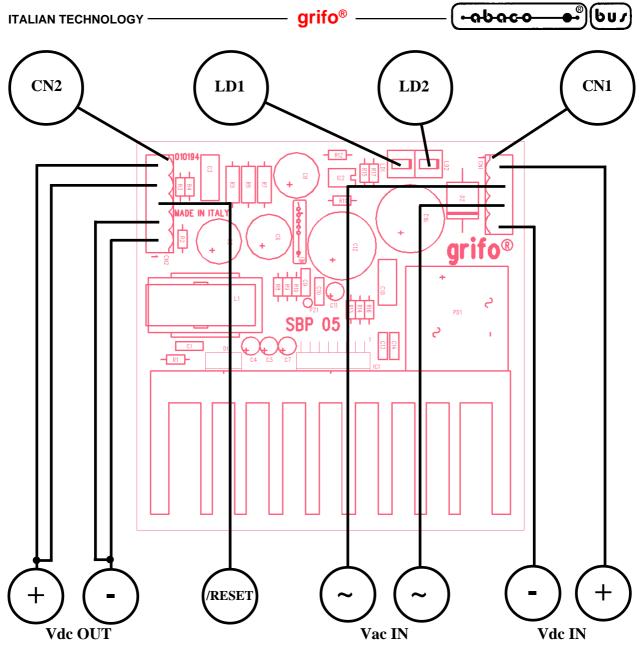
DISPOSIZIONE LED, CONNETTORI, TENSIONI, ECC.
